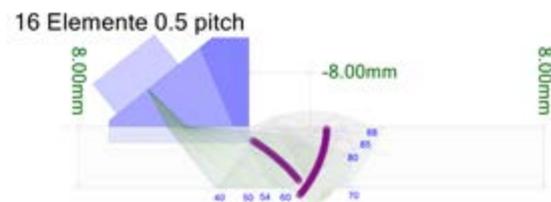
d. LOW-Profile-PAUT-Prüfkopf (8 mm Aperturlänge) auf 8 mm Wanddicke
